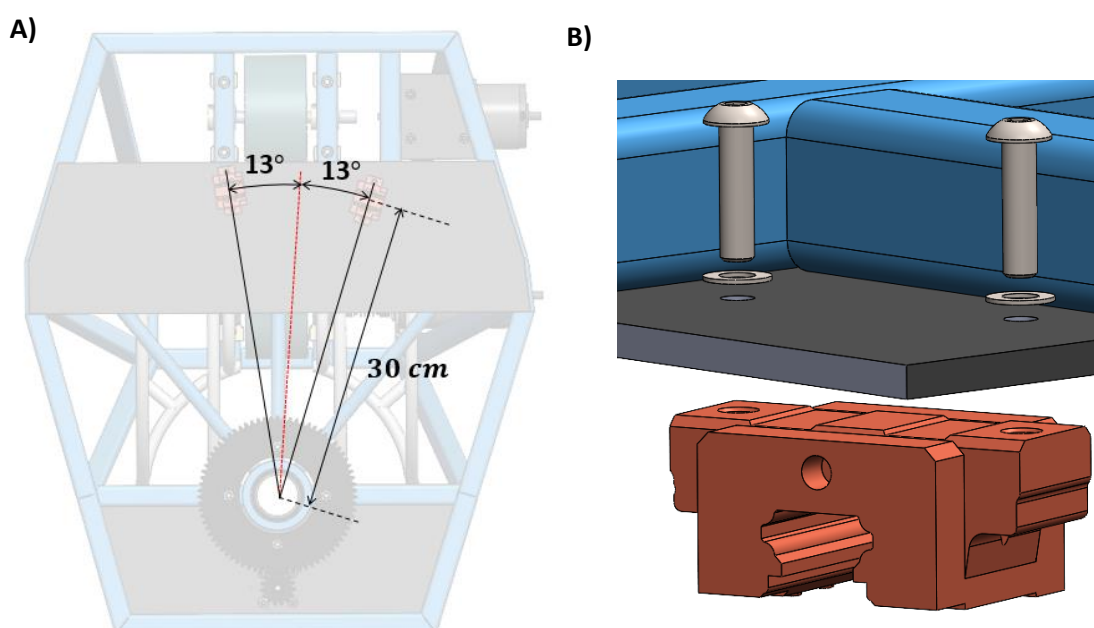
A) Disposició corredores al xassís; B) Vista explosionada de l'assemblatge de la corredora.
